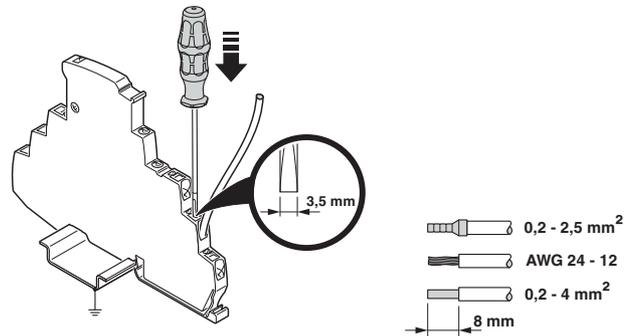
Variante de conexión push-in (ancho de construcción 6 mm)
